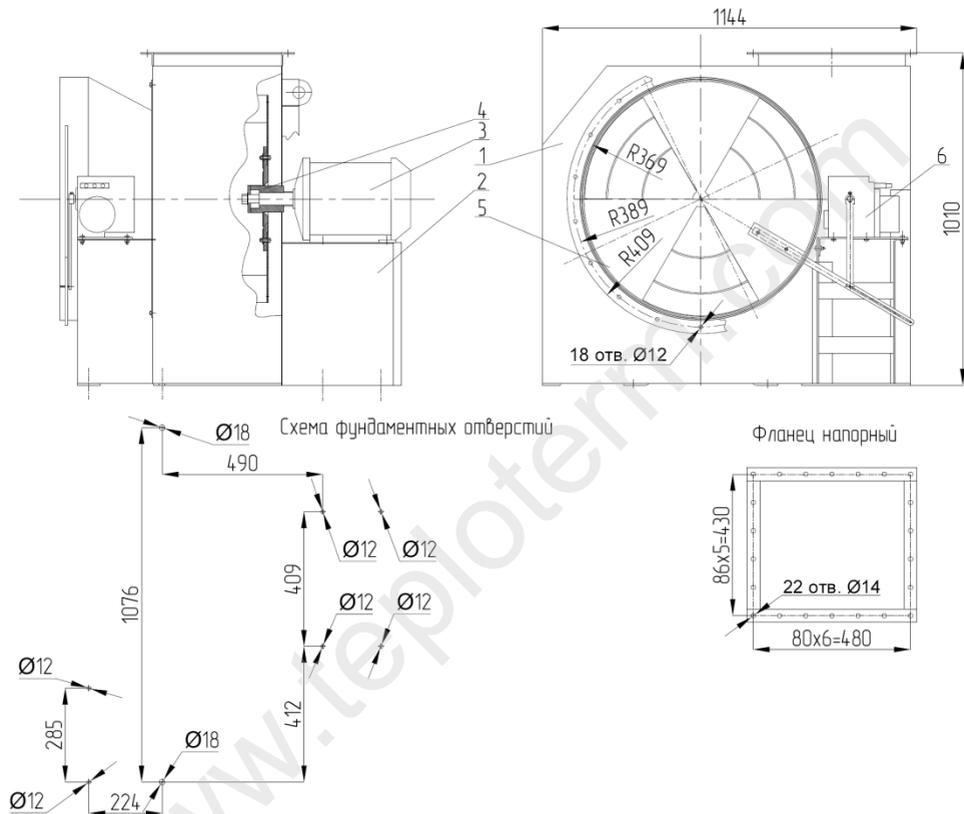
Вентилятор ВД-6,3 (1-корпус, 2-рама, 3-электродвигатель, 4-рабочее колесо, 5-аппарат шиберный, 6- привод шибера.)
